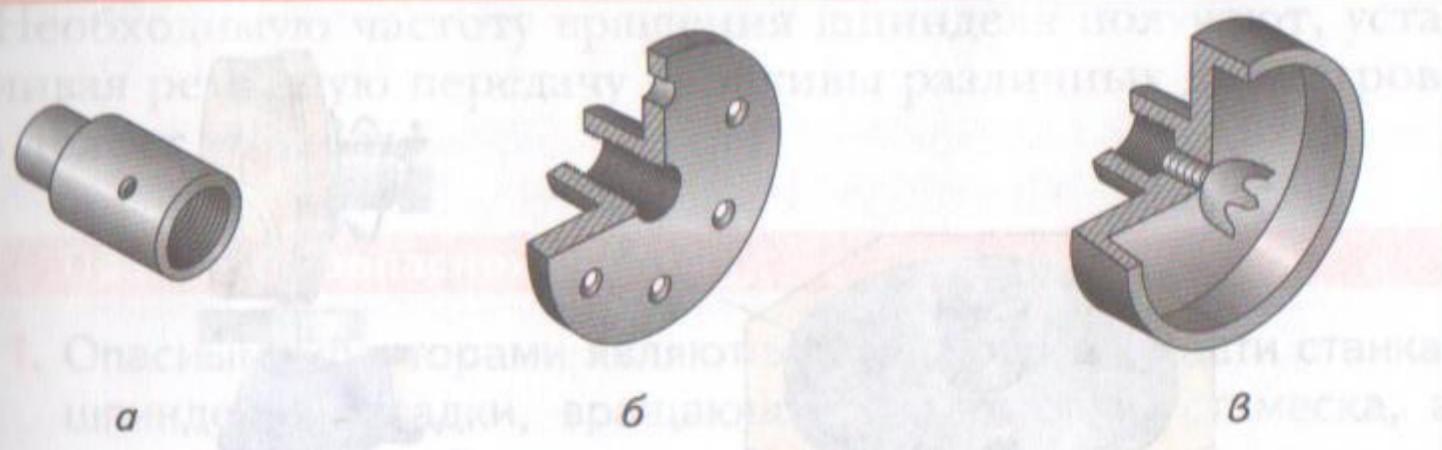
Шпиндельные приспособления для крепления заготовок при точении:
